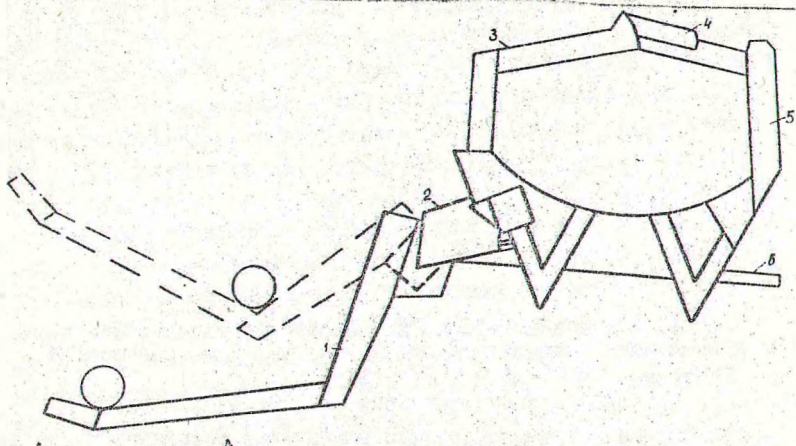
Погрузочно-формирующее устройство: 1 - погрузочный рычаг; 2 - сектор; 3 - обвязочный рычаг; 4 - гидроцилиндр обвязочного рычага; 5 - остоу; 6 - механизм затяжки рычагов с гидроприводом.
